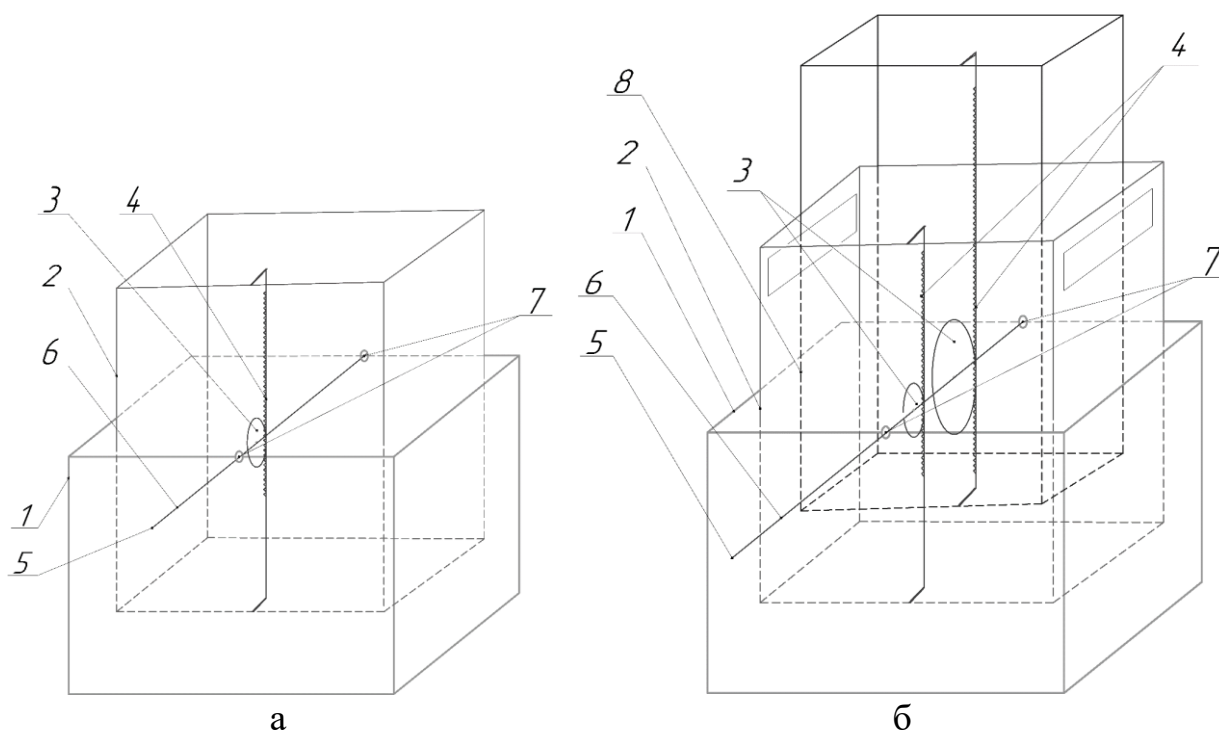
Варианты конструкций выдвижных механизмов с зубчатой передачей: 1) нижняя опорная секция; 2) первая подвижная секция; 3) зубчатое колесо; 4) зубчатая рейка; 5) место крепления привода*; 6) валы зубчатых колес; 7) радиальные подшипники; 8) вторая подвижная секция
